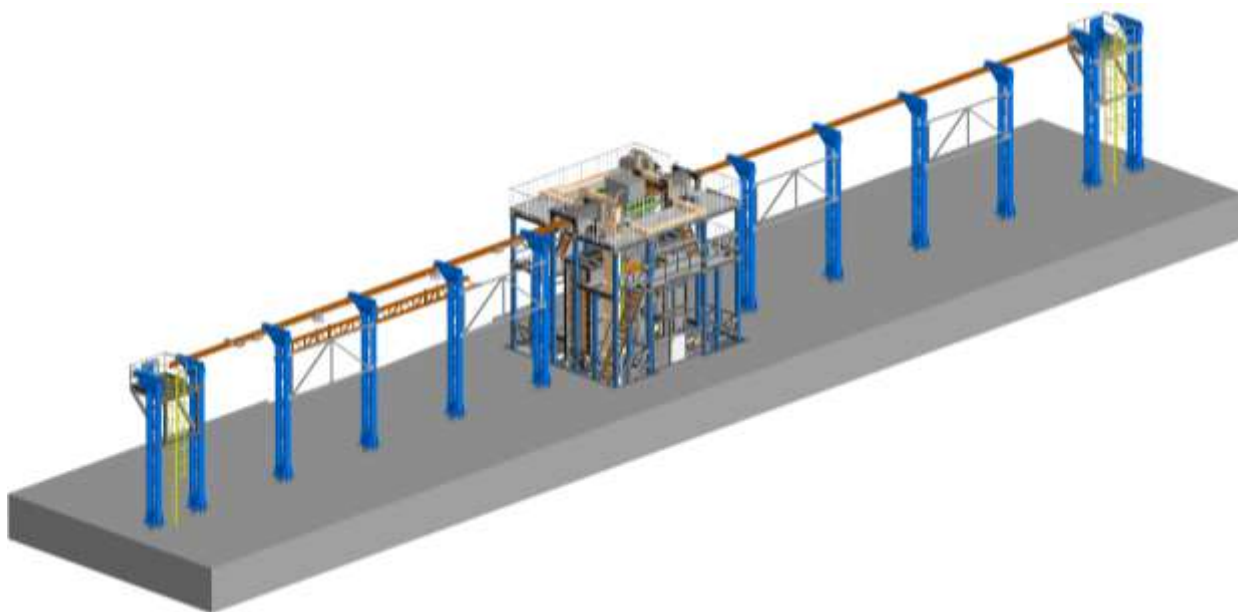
УПТ для черновой формообразующей обработки и упрочняющей обработки
